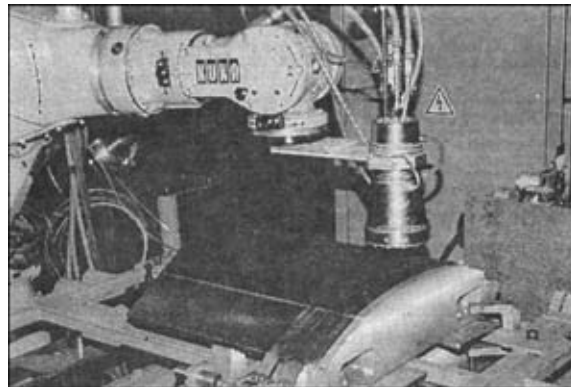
Светолучевое оборудование для сварки и пайки
